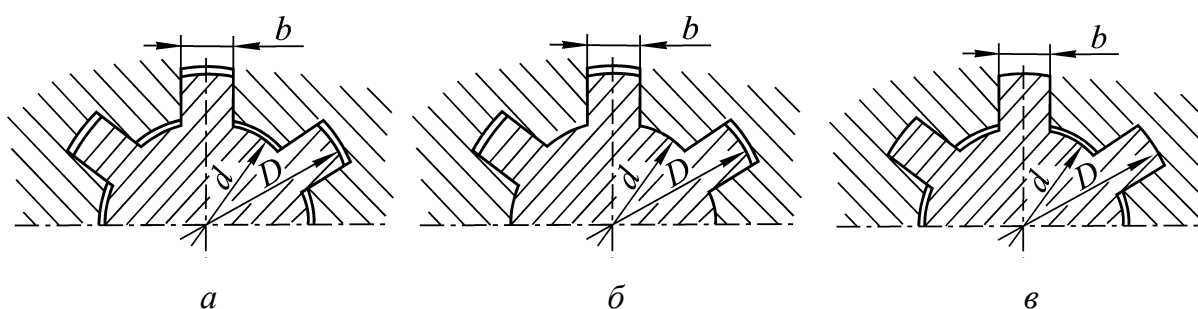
Способы центрирования шлицевых соединений с прямобоочным профилем:
